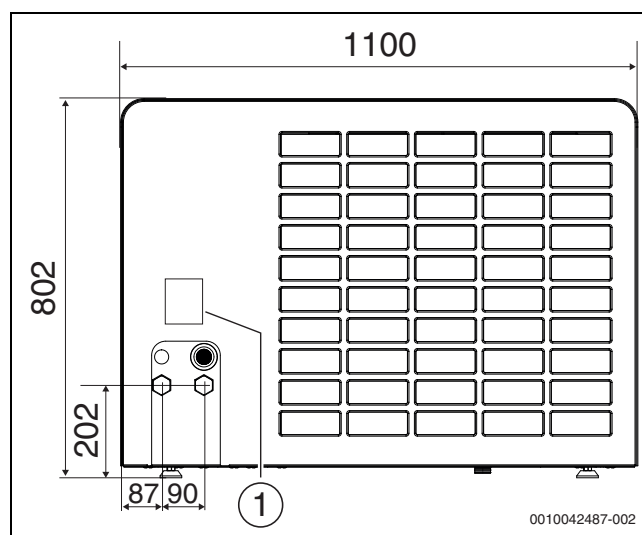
Dimensions et raccords de la pompe à chaleur, arrière
